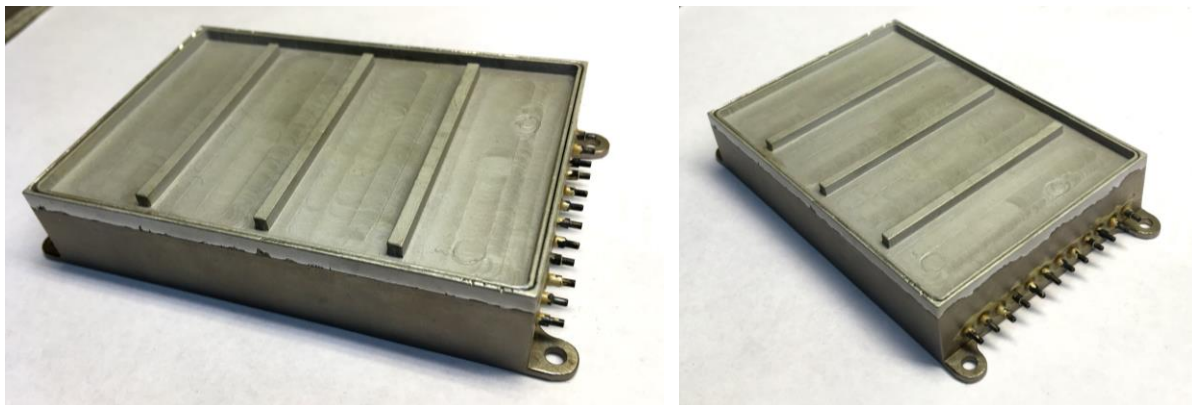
Внешний вид типовых корпусов микросборок после пайки-сборки
